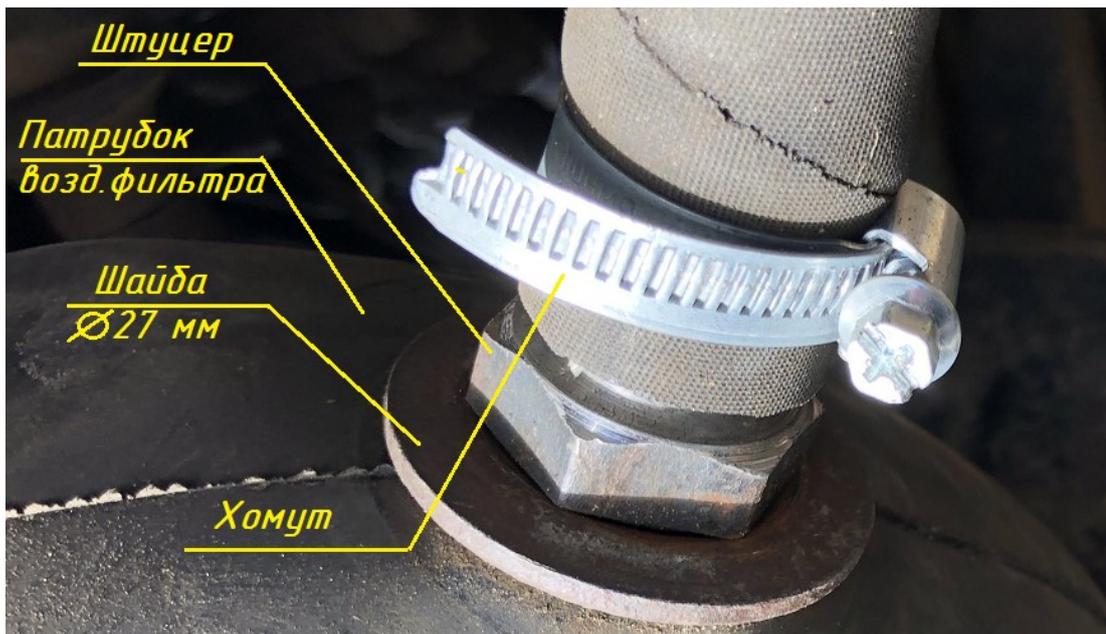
Установка Штуцера 7408-3509273 в патрубок 5320-1109445.
